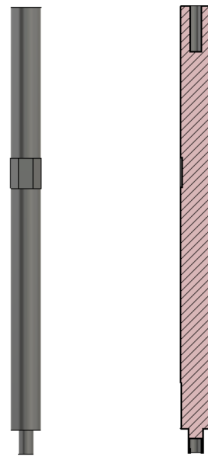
Separador vertical: Cilindro inferior y vista en sección.
